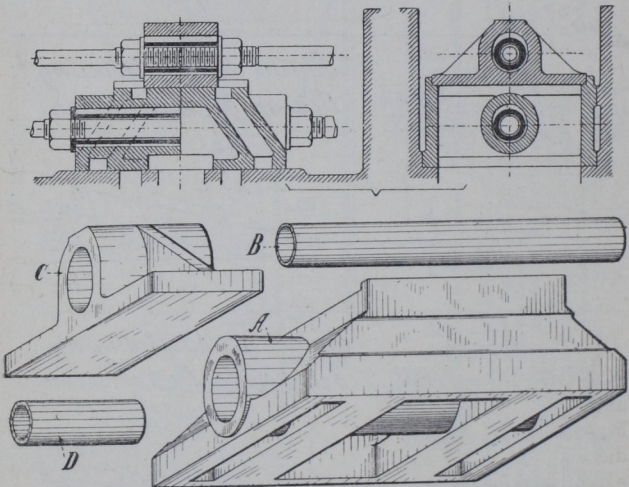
285. Teile zur Doppelschiebersteuerung mit fixer Expansion.
